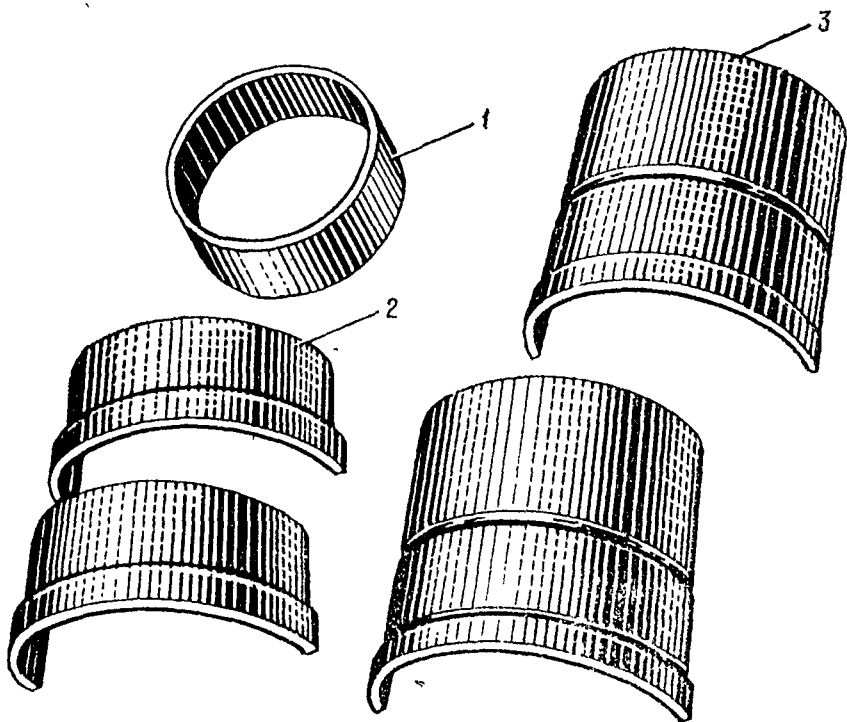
Предохранительные оправки для сборки уплотнительного пакета: 1 — цилиндрическая оправка 64600/Д-45 на верхнюю резьбу штока; 2 — короткая разъемная оправка 64600/Д-44 или Л-1/1923 на нижнюю резьбу цилиндра; 3 — длинная разъемная оправка 64600/Д-43 или 635/479 на внутреннюю резьбу цилиндра
